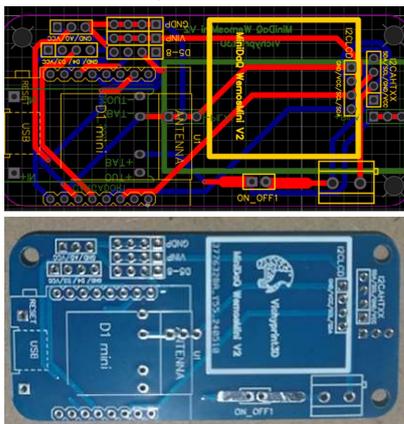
Arriba, diseño en software de la PCB, abajo, placa final
